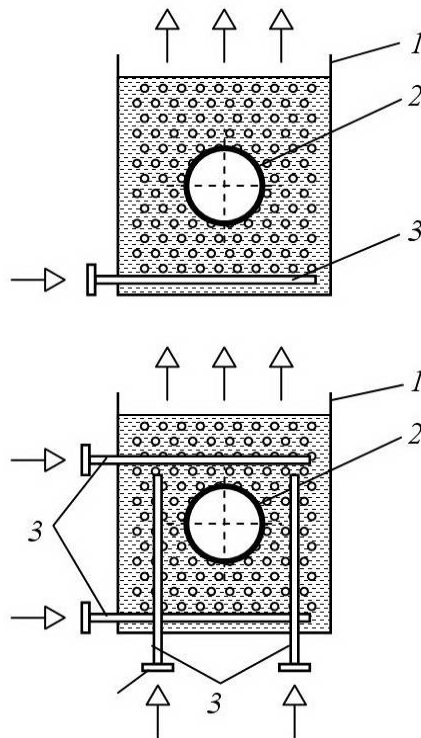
Поперечний переріз охолоджувальних пристроїв згідно з пат. № UA69281U та UA79165U: 1 – ванна; 2 – охолоджуваний виріб; 3 – розпилювачі; 4 – механізми регулювання положення розпилювачів
